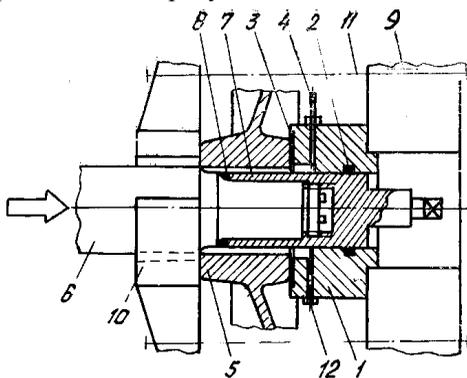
Сборка цилиндрических соединений с помощью нагнетания масла в зону сопряжения с натягом цельнокатаного колеса 5 и оси 6 формируемой колёсной пары; фальшвалом 7 с уплотнением 8. На подвижную станину 9 пресса, закреплённую на объёмлющей раме последнего, монтируется закрепительная траверса 10 механизмом прижатия 11. От плунжера пресса (на рисунке условно не показан) усилие запрессовки P_3 передаётся на торец свободного конца сопрягаемой оси 6 колёсной пары. Для слива масла из навесной гидроголовки высокого давления предусмотрен клапан 12.
